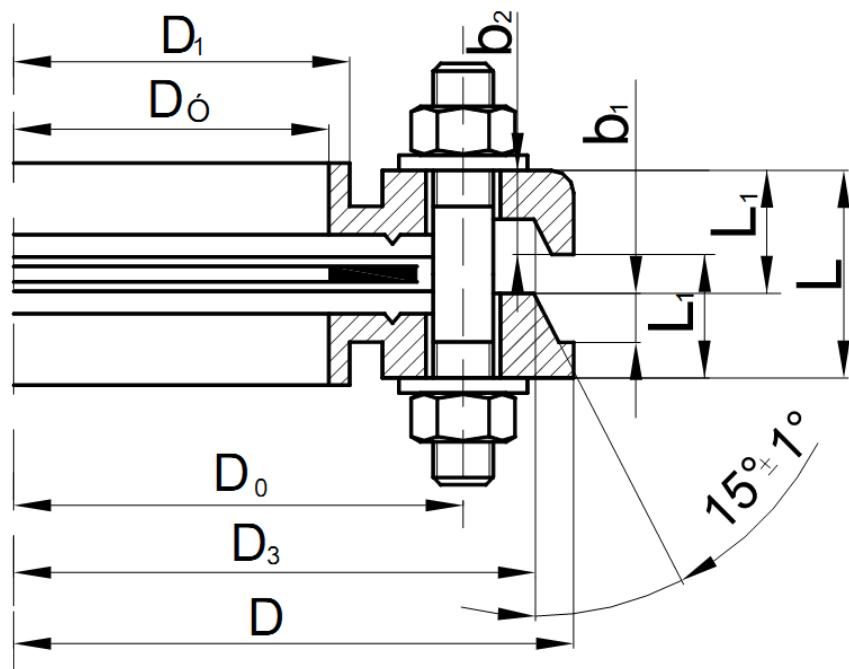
Соединение с плоской металлической прокладкой и канавочно-клиновым уплотняющим профилем
